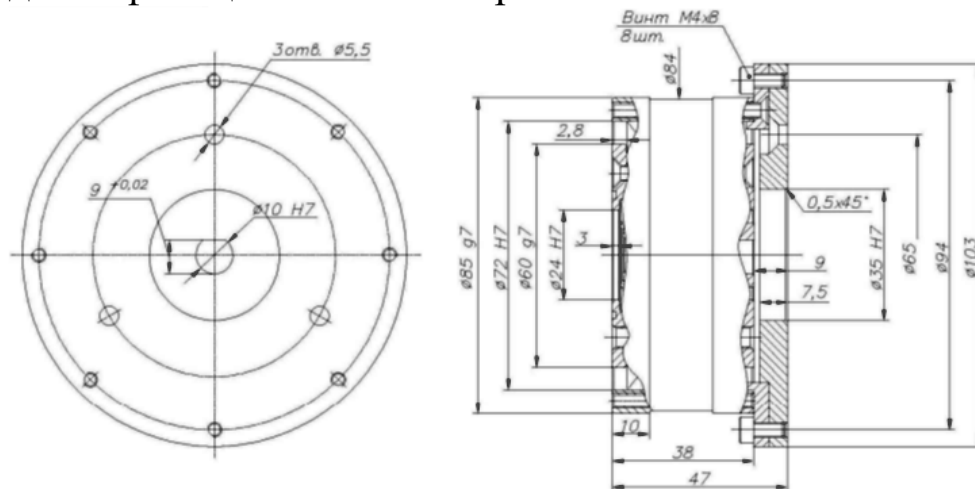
Сборочный чертеж редуктора и переходного фланца
